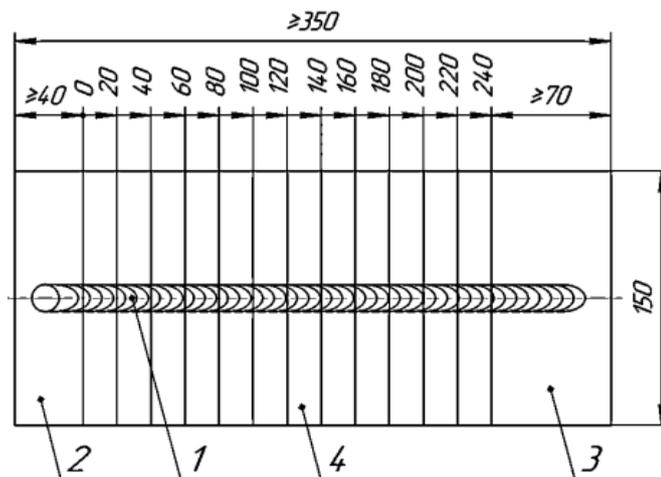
Схема збирання складових пластин для наплавлення: 1 – наплавлений валик, 2 – приставна планка (для початку наплавленого валика); 3 – приставна планка (для кінця наплавленого валика), 4 – складова пластина (брусок)
